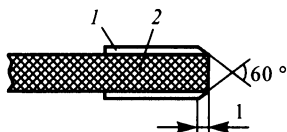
Концевая часть вилочного печатного соединителя платы:
